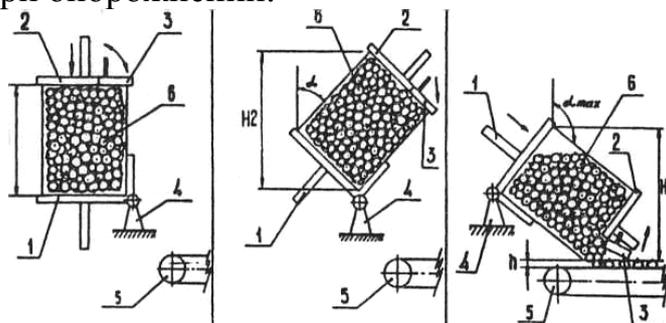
Принцип действия гравитационного опорожнителя: а - контейнер в исходном положении; б - поворот контейнера; в - выгрузка продукции; 1 - поворотная рама; 2 - верхняя крышка поворотной рамы; 3 - откидная часть крышки; 4 - консоль с осью поворота; 5 - транспортер; 6 - контейнер с продукцией.
